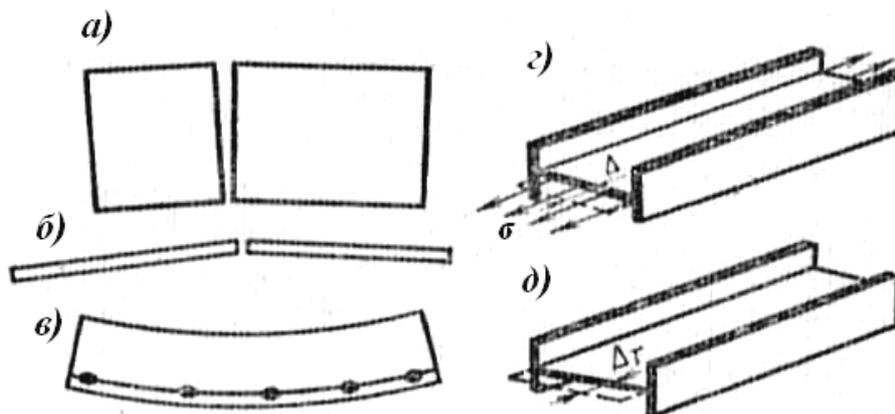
Создание перемещений, противоположных сварочным
